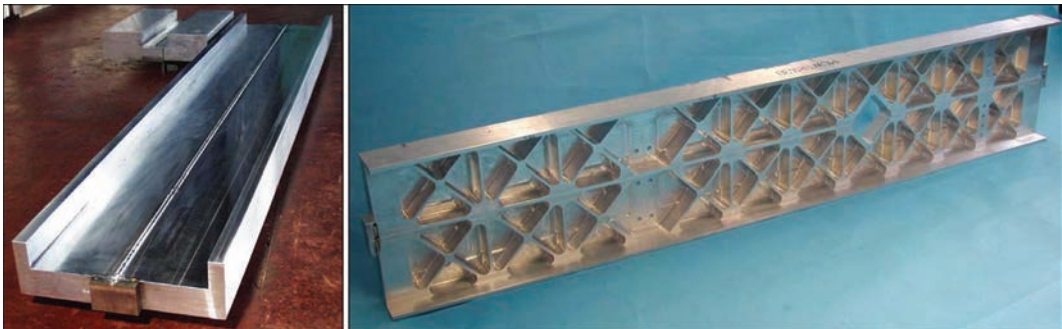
Сваренная заготовка (слева) балки авиационного крыла (справа — после механической обработки) из высокопрочного алюминиевого сплава
